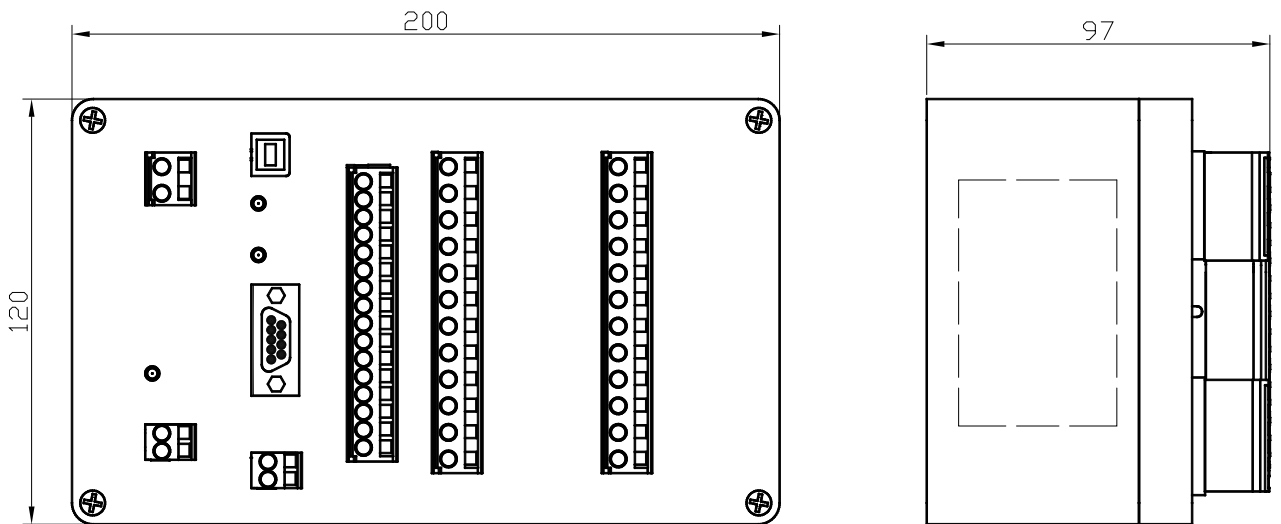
Габаритные размеры контроллера с двумя МСД
